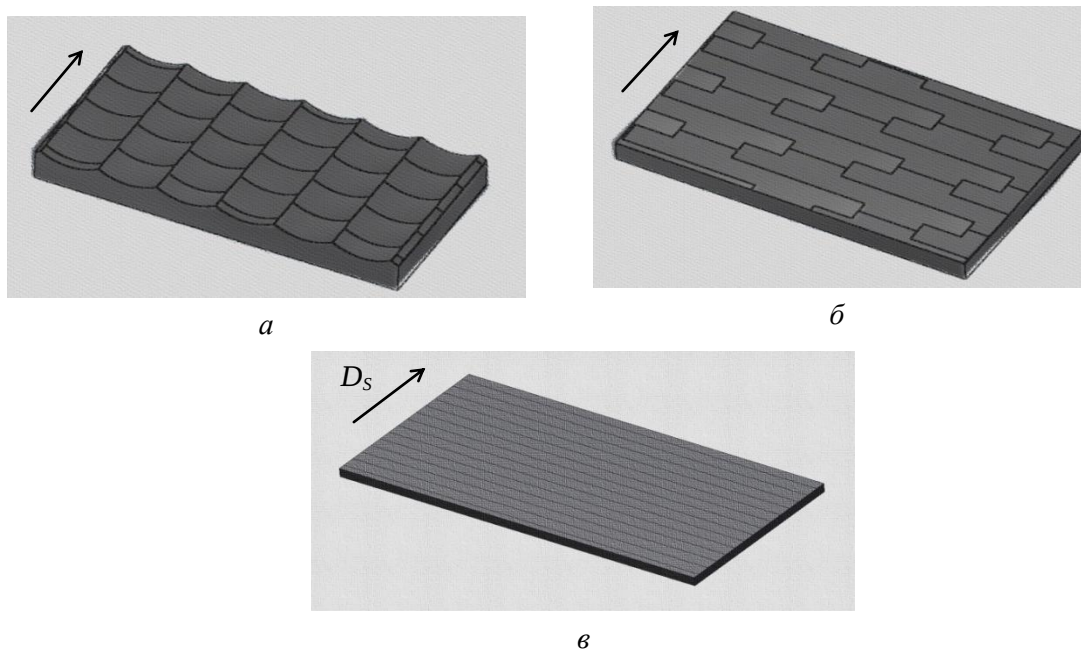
Вид поверхностей, обработанных фрезами с режущей кромкой разного профиля:
